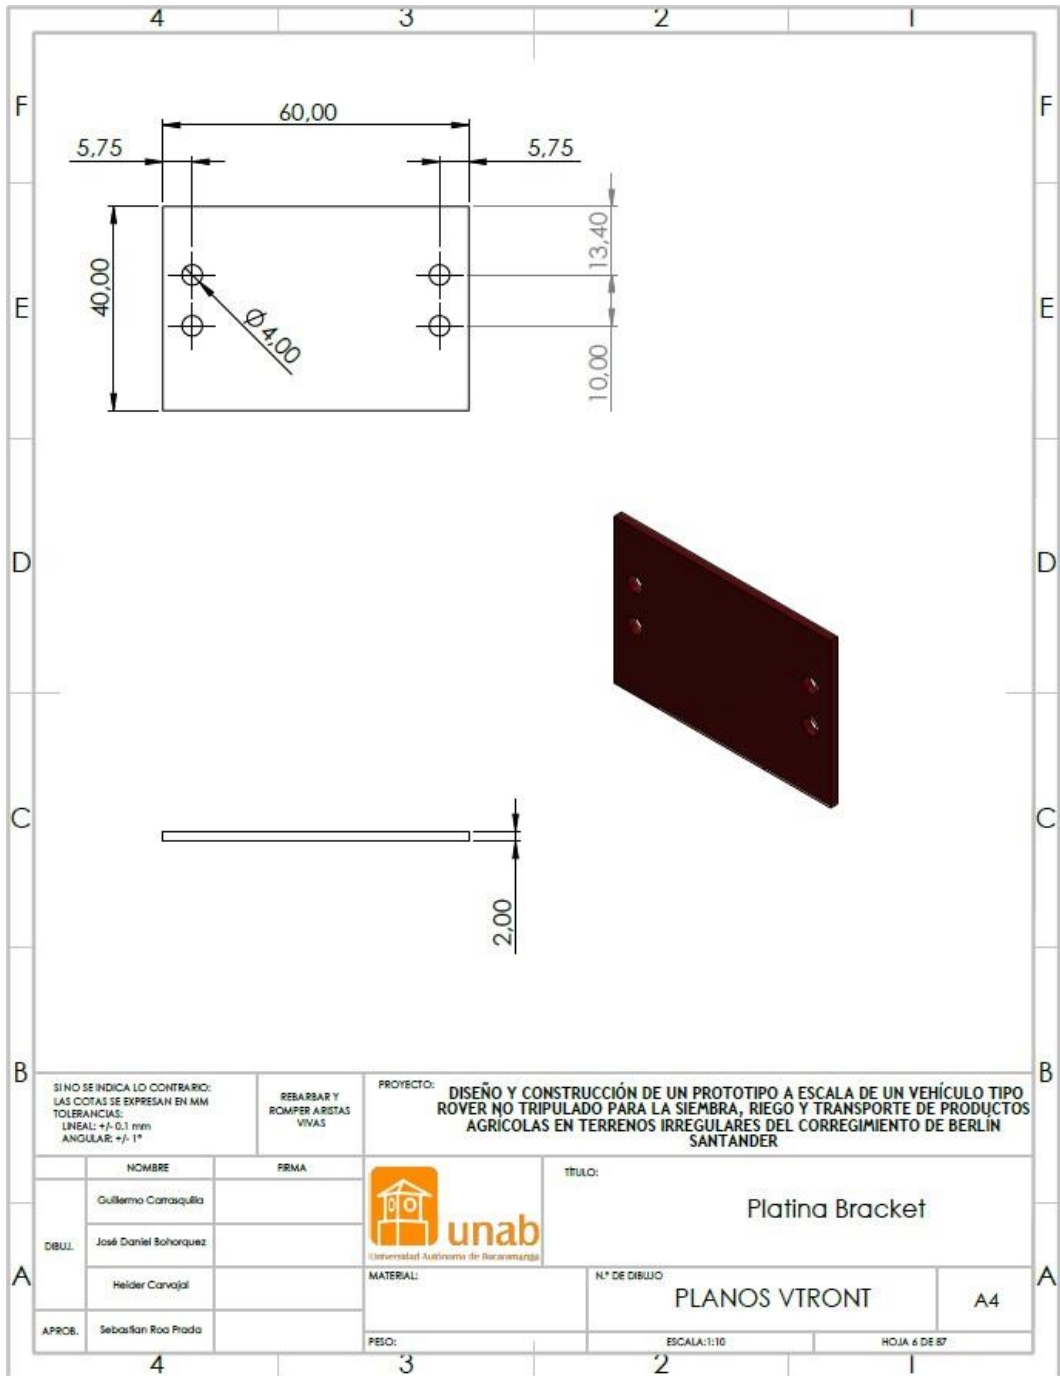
Plano de la platina para acople de los brackets de servo.
